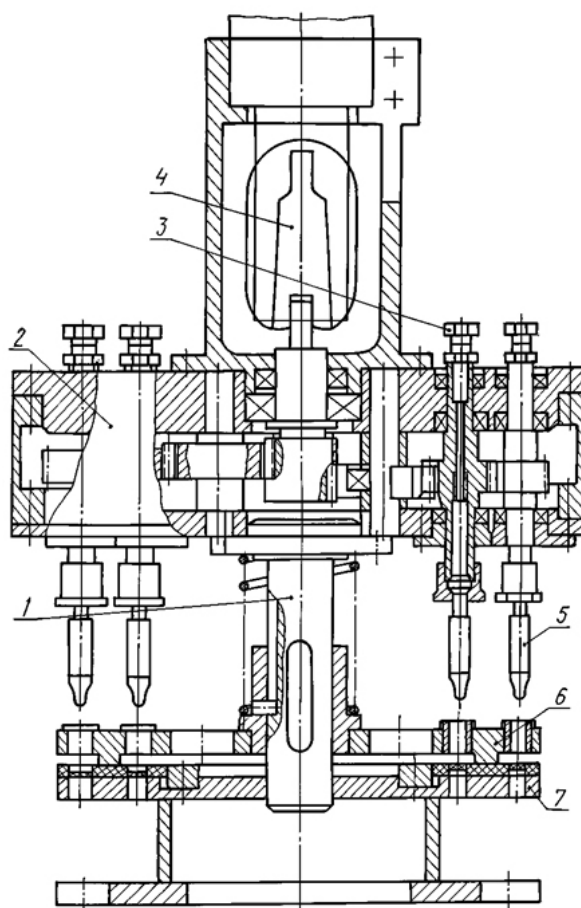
Принципиальная схема приспособления для сверления отверстий в накладке ведомого диска сцепления: 1 – оправка; 2 – редуктор; 3 – болт; 4 – центр; 5 – сверло; 6 – кондукторная плита; 7 – подставка
